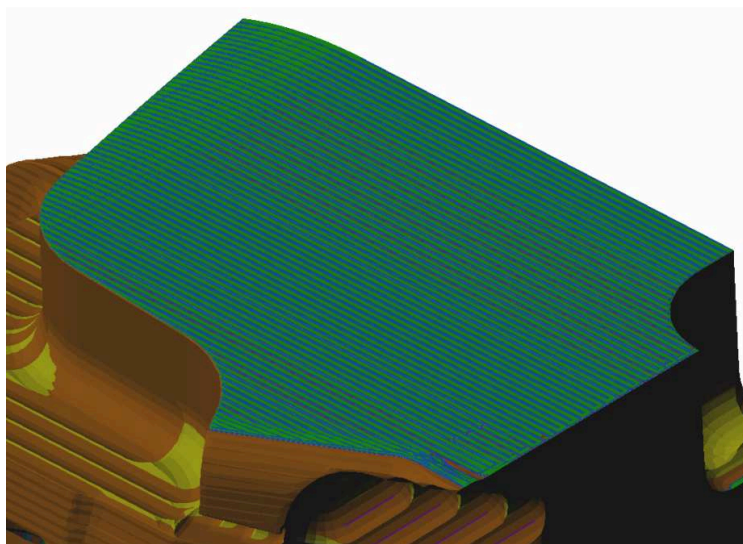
Čas obrábění strategie Spiral-Milling
